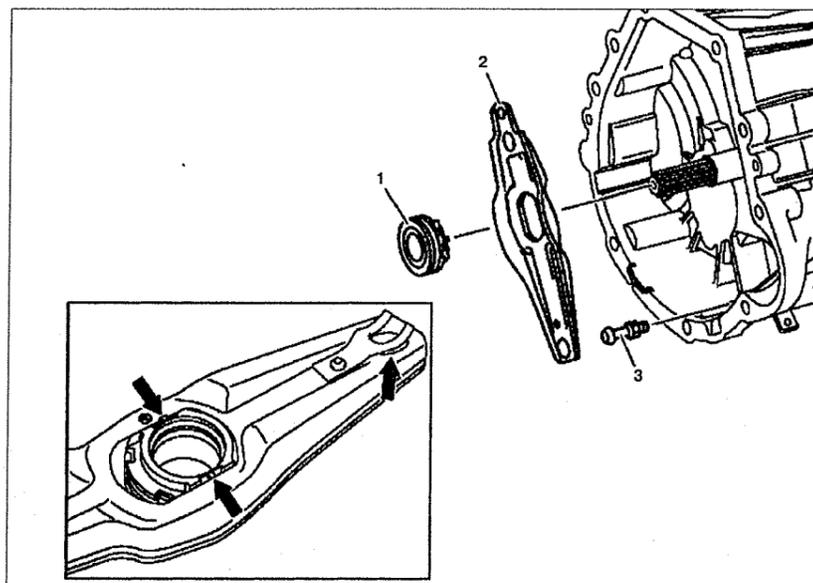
Рычаг выключения сцепления (только на автомобилях с двигателями 111.948 и 601.970):
